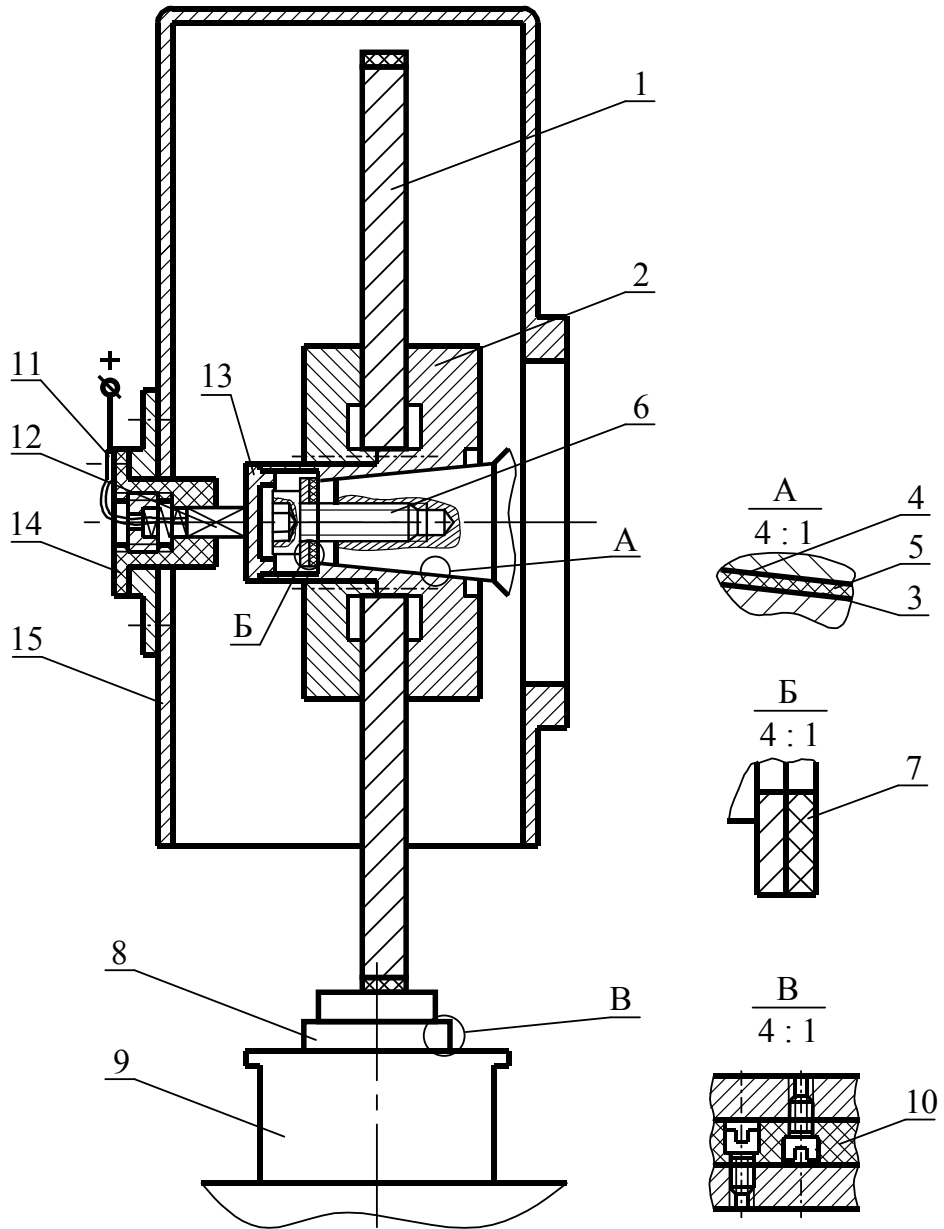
Схема электрической изоляции шлифовального круга от шпинделя плоскошлифовального станка
